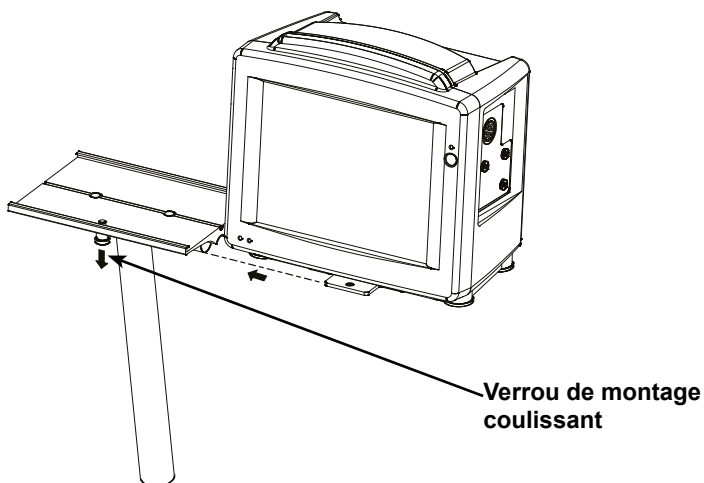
Vue avant du chariot mobile et emplacement du verrou coulissant
